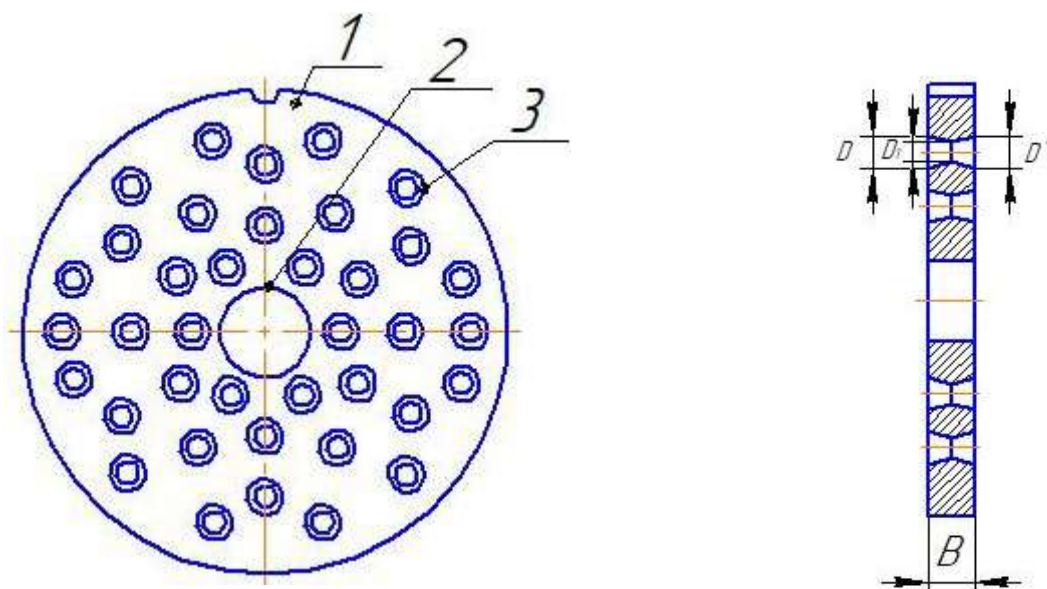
Решетка к устройству для измельчения мяса
